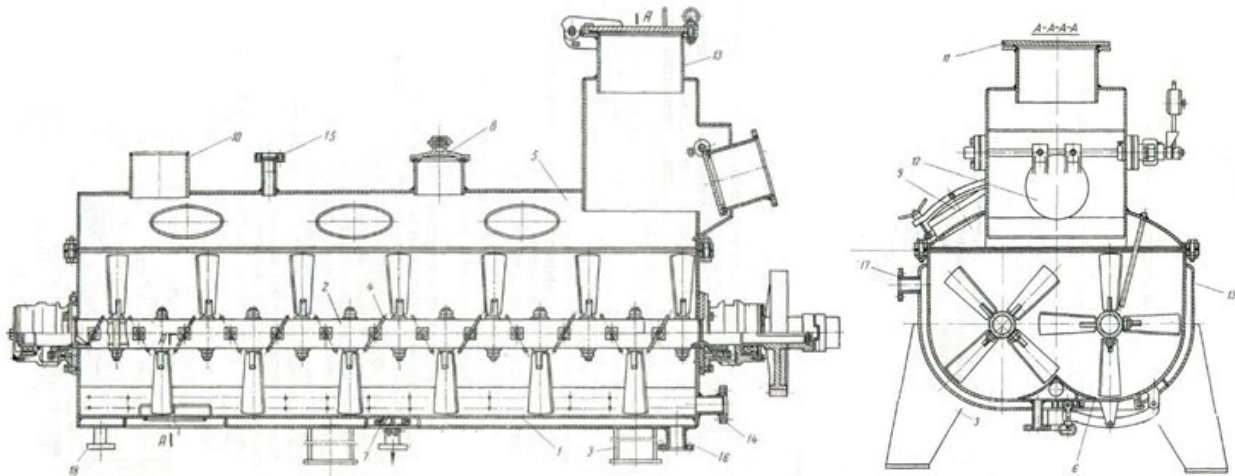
Стерилізатор для висівок конструкції Українського науково-дослідного інституту харчової промисловості: 1 - корпус; 2 - ведений вал; 3 - лапа; 4 лопать; 5 - кришка стерилізатора; 6 – розвантажувальний люк; 7 - патрубок спускання промивної води; 8 - люк для завантаження посівної культури; 9 – люк для миття корпусу стерилізатора; 10 - патрубок для виходу повітря та пари; 11 - люк для завантаження середовища; 12 - клапан повітряного патрубку; 13 - охолоджуватиа сорочка; 14 - патрубок для подачі пари; 15 - патрубок подачі стерильної води; 16 - патрубок для підведення охолоджувальної води; 17 - патрубок для відведення води з охолоджувальної сорочки; 18 - патрубок для відведення конденсату
